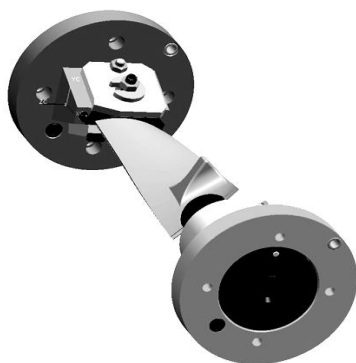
Шарнирное станочное приспособление для крепления лопатки
